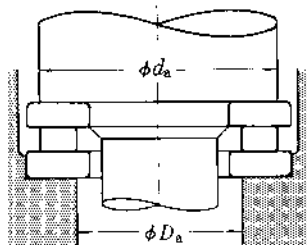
Диаметры поверхности опора для упорных роликоподшипников
